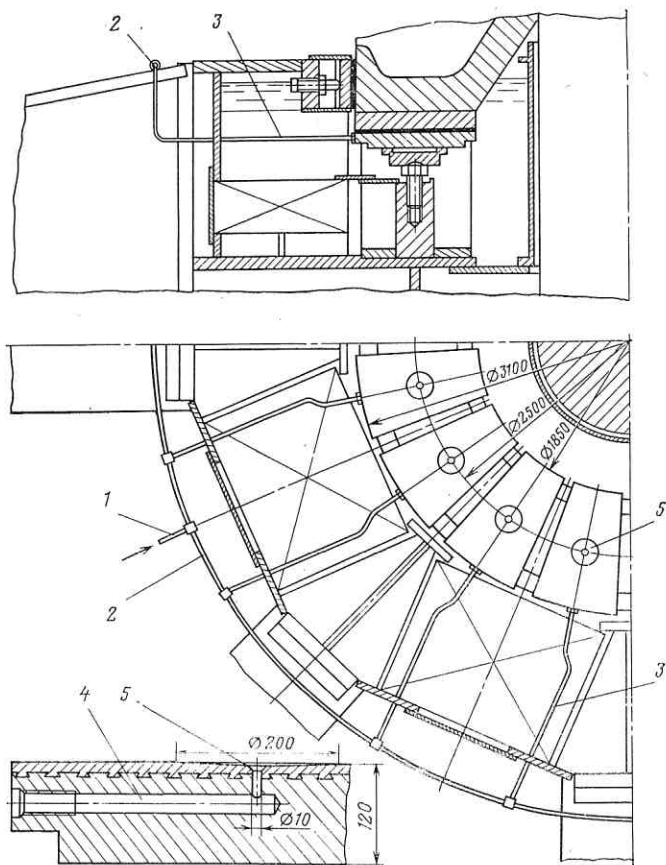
Подпятник с принудительной подачей смазки к поверхностям трения: 1 — напорный трубопровод; 2 — кольцевой коллектор; 3 — соединительные трубки; 4 — радиальный канал в сегменте; 5 — лунка на рабочей поверхности
